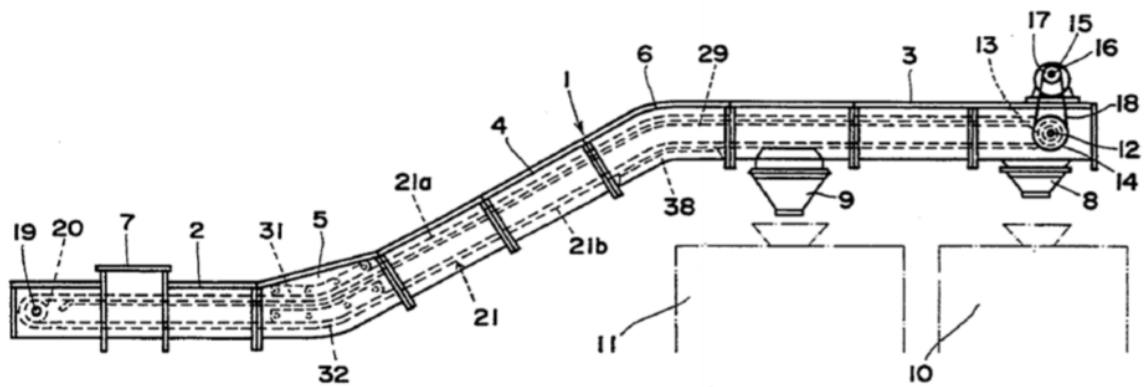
Боковий підйомний пристрій скребкового транспортера
